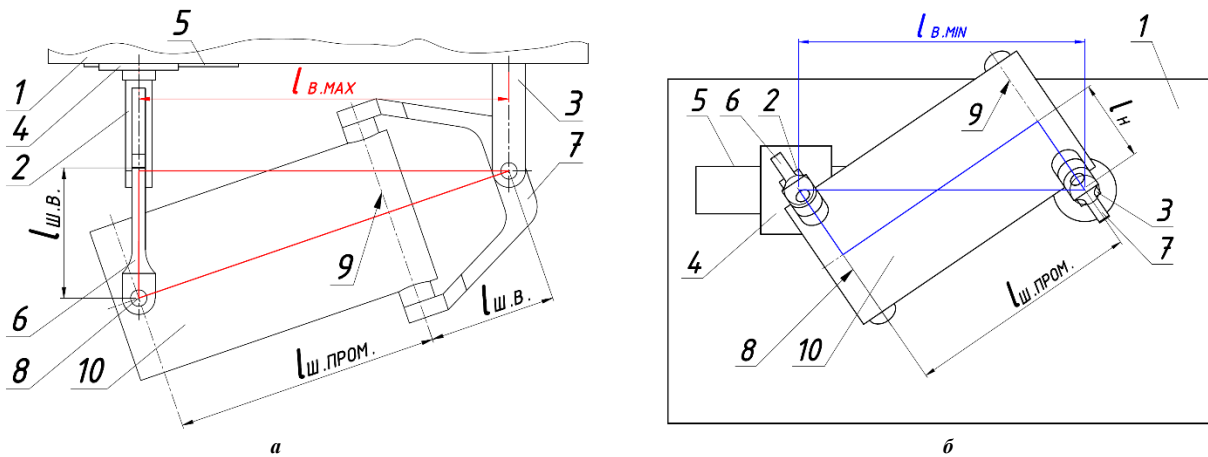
Машини для обробки деталей: а – вид зверху, б – вид спереду
